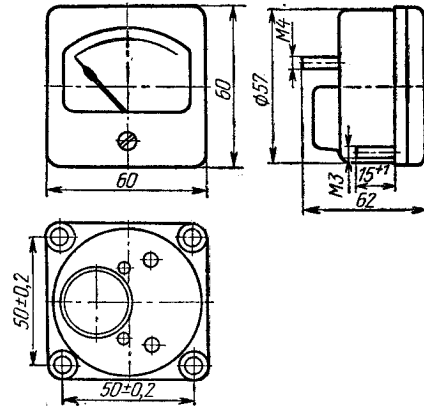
Габаритный чертеж прибора типа М4202.
